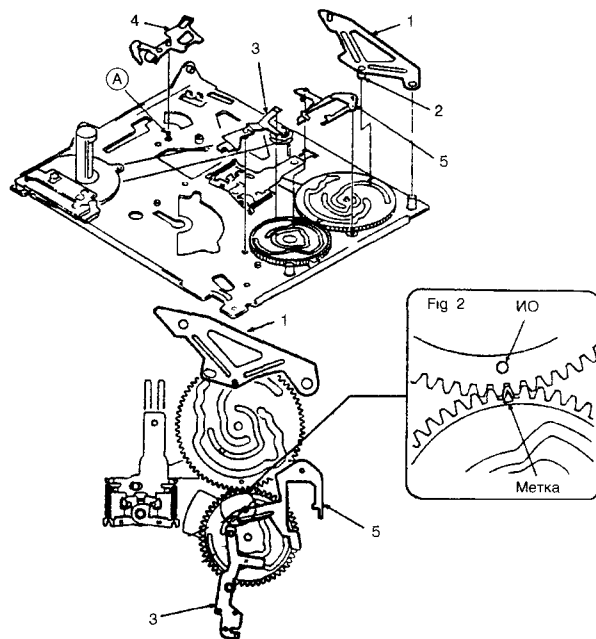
Демонтаж и установка рычага LS, рычага привода НС, пластины прижима и пластины регулятора натяжения
